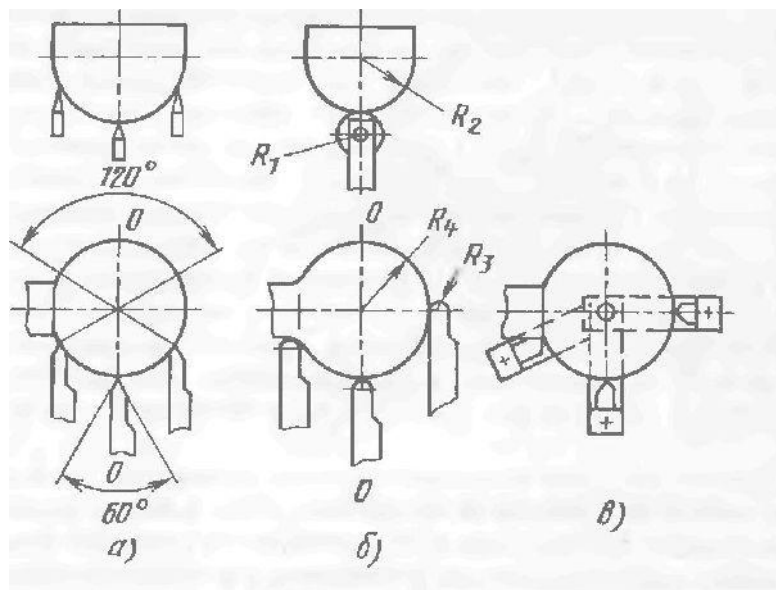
Приспособления с поступательными (а,б) и вращательным (в) движением резца.
